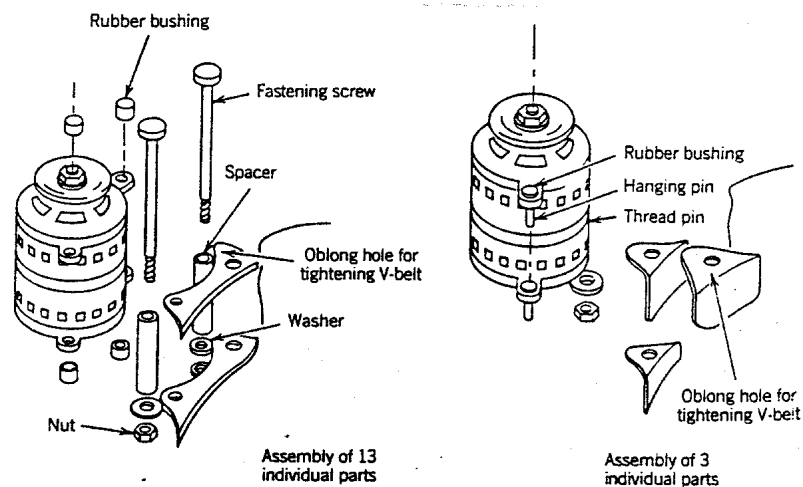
Design para automação aplicado à montagem de um pequeno motor de uma máquina de lavar.
